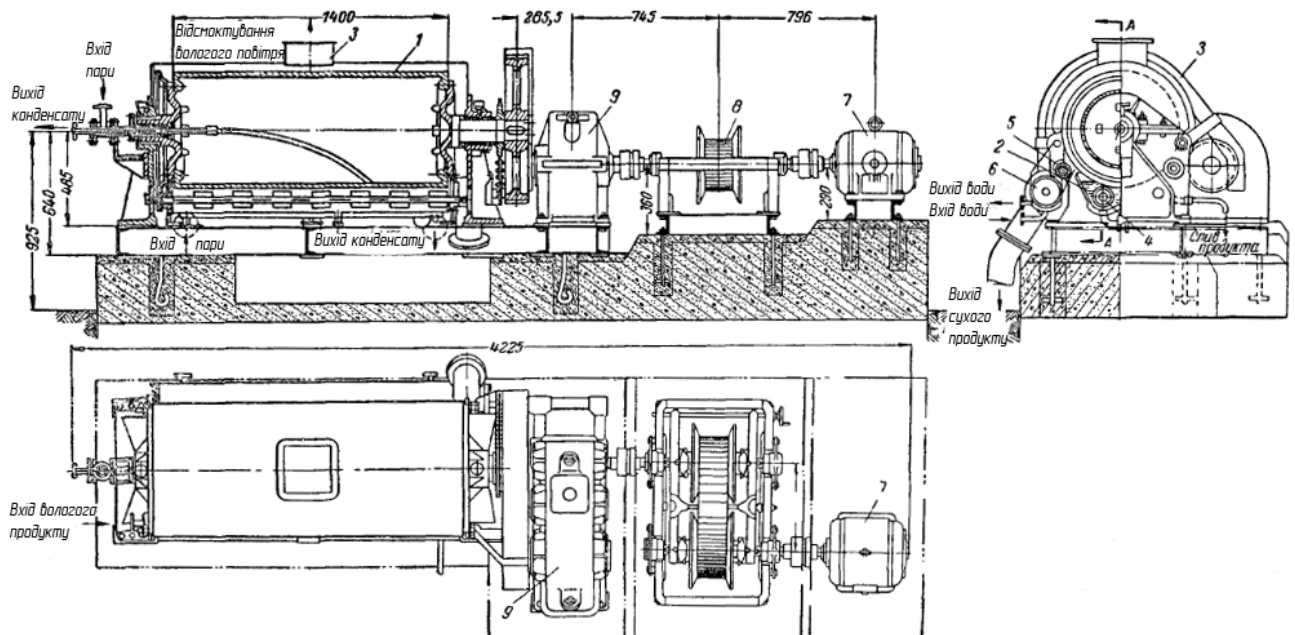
Сушарка одновальцова атмосферна: 1 – сушильний валець; 2 – місткість живлячого пристрою; 3 – кожух; 4 – перемішуючий пристрій; 5 – ножі шкребкового пристрою; 6 – шнек; 7 – електродвигун; 8 – варіатор кількості обертів; 9 - редуктор
